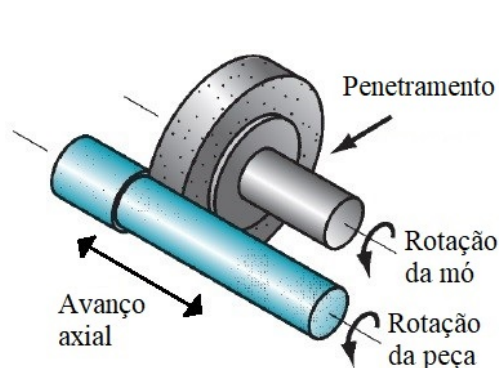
Retificação cilíndrica exterior (Adaptado de [5]).
